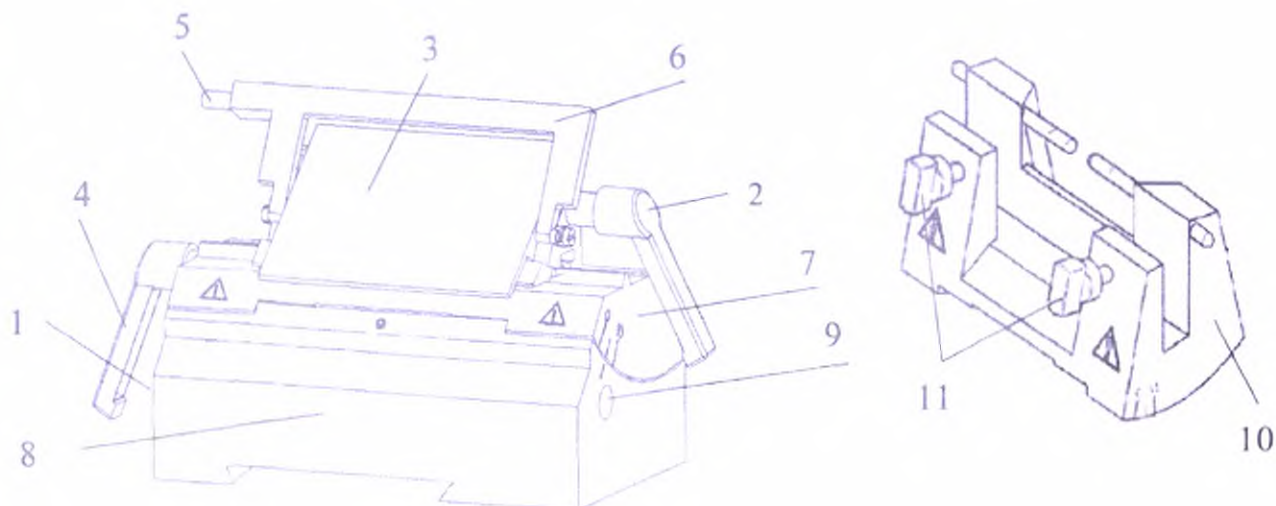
Установка держателя стального ножа, держателя лезвия и его основания
